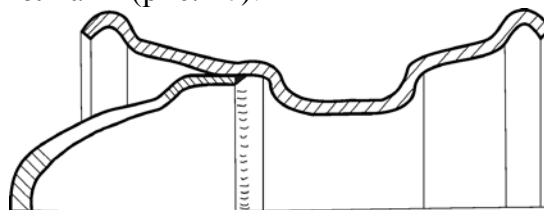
Конструкция обода грузового колеса однокомпонентной конструкции для бескамерных шин
